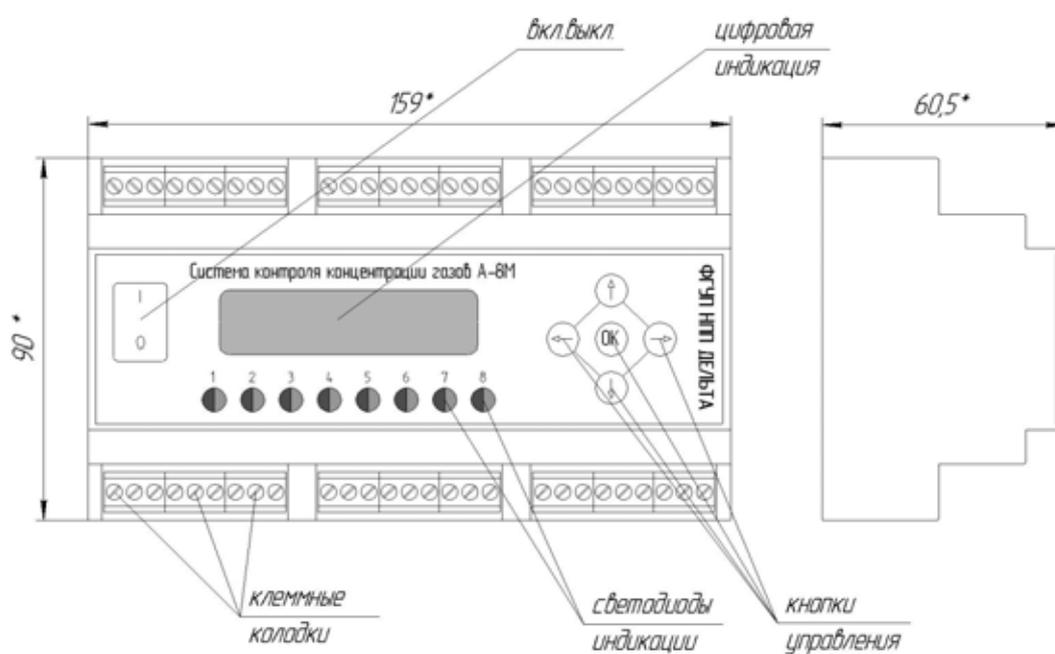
Внешний вид и габаритные размеры пульта контроля.
